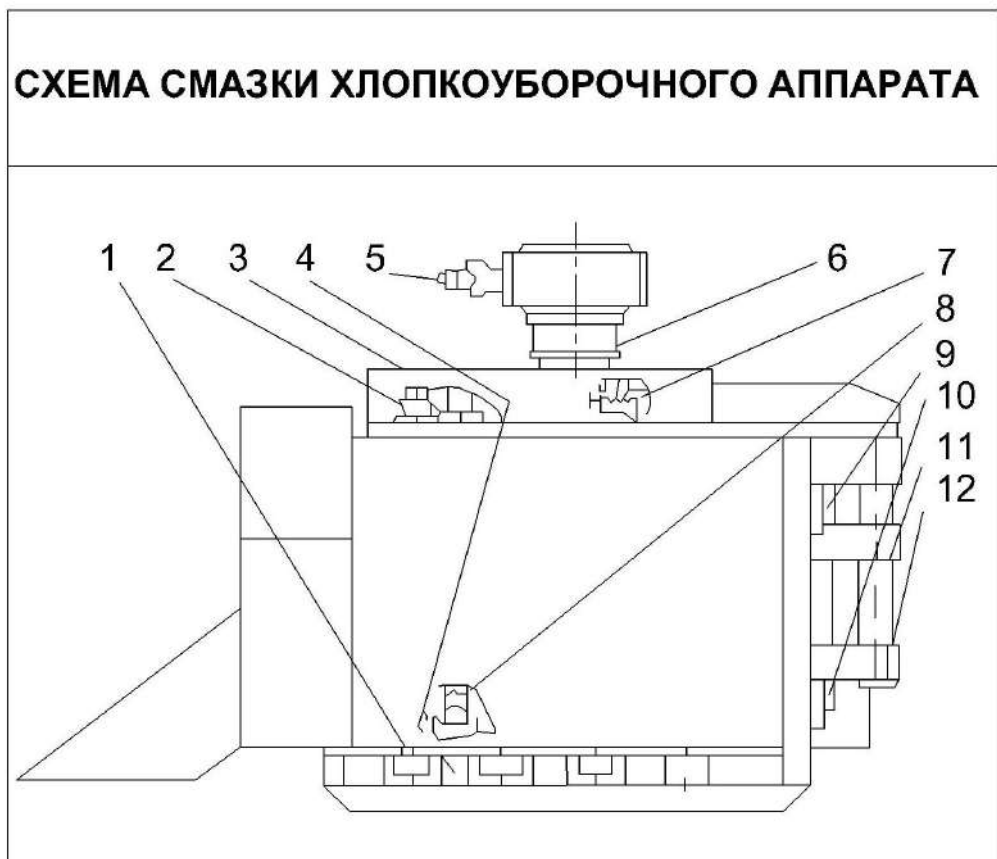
Схема смазки хлопкоуборочного аппарата
